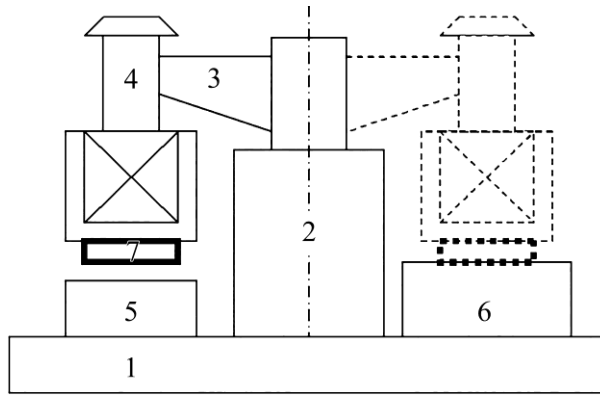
Установка для закалки деталей: 1 – бак-станина; 2 – поворотная колонна; 3 – плечо; 4 – электромагнит; 5 – ванна; 6 – подставка; 7 – обрабатываемая деталь [127].
